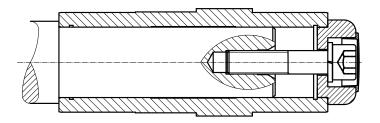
Getriebe auf Welle mit Anlageschulter mit Befestigungselement befestigt
